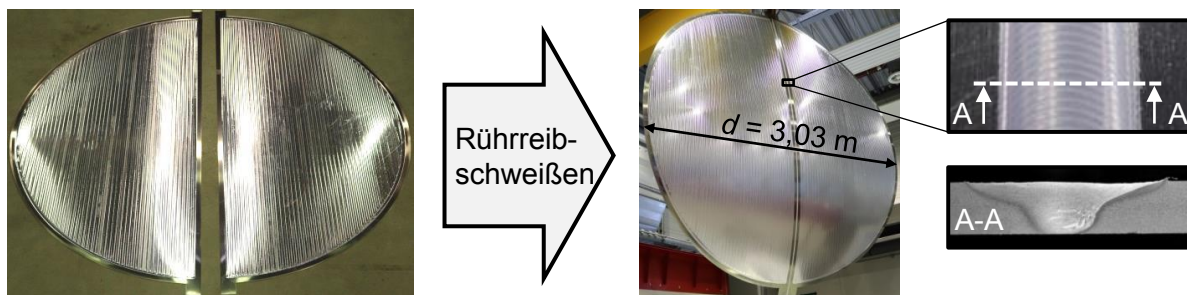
Gefräste „Halbronden“ vor dem Schweißen (links), Rührreibgeschweißte Ronde mit Detailansicht und Querschliff der Schweißnaht (rechts)
